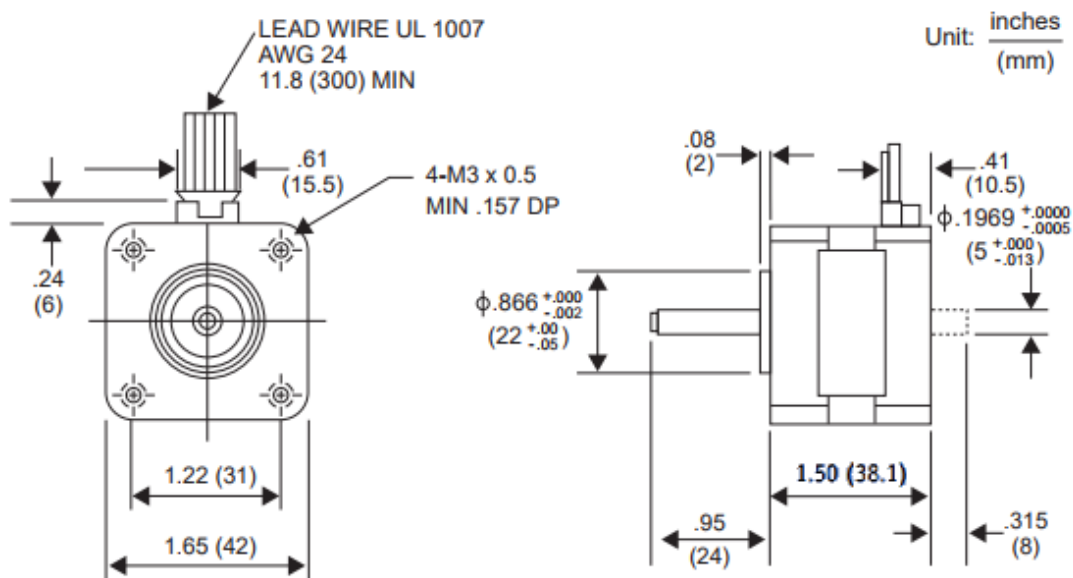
Desenho do motor de passo 17PM-K301V
